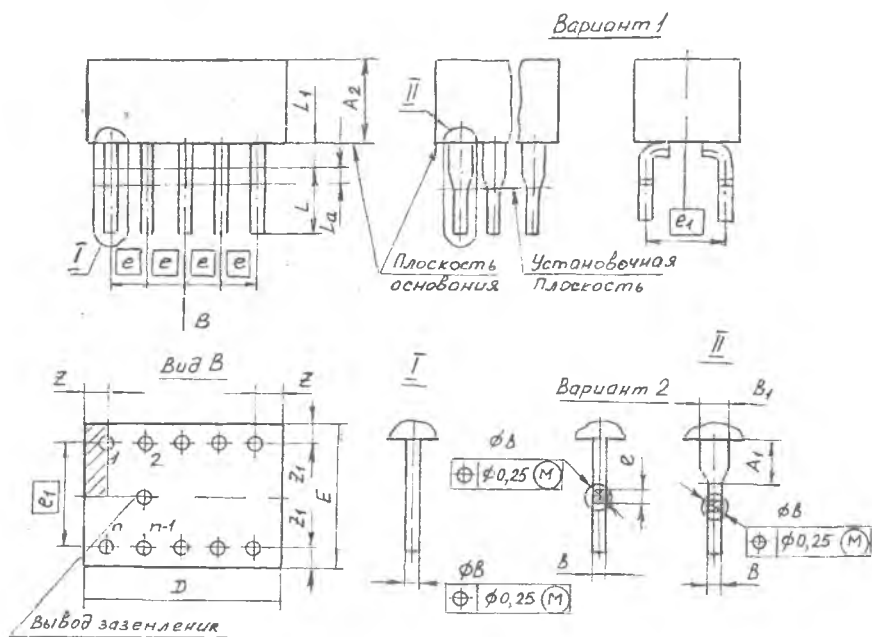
Конструкция корпуса типа 1 подтипа 2
